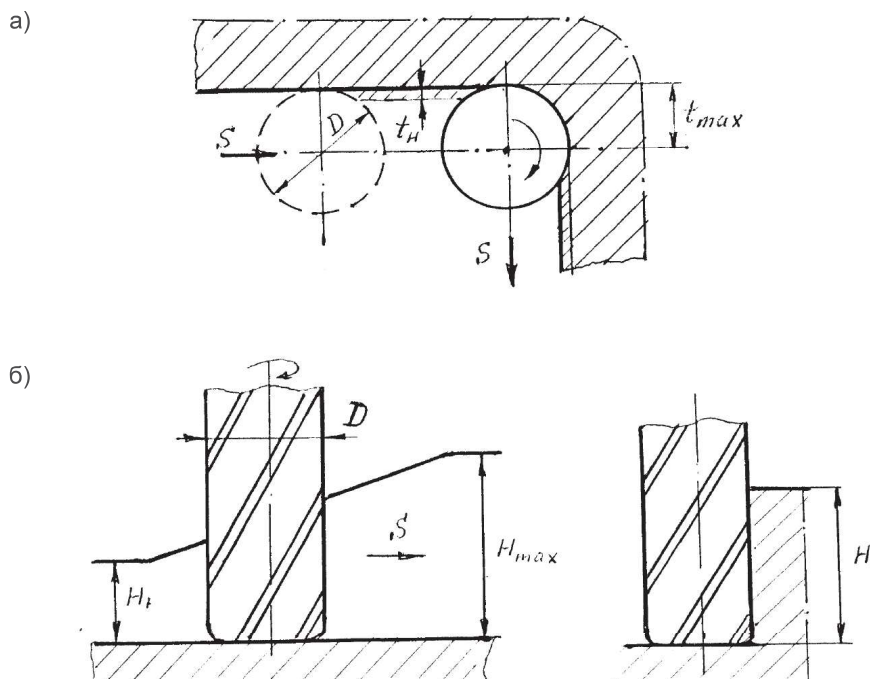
Изменение параметров обработки при контурном фрезеровании концевой фрезой: а) изменение глубины резания при перемене направления движения, б) изменение ширины фрезерования при изменении высоты стенки
